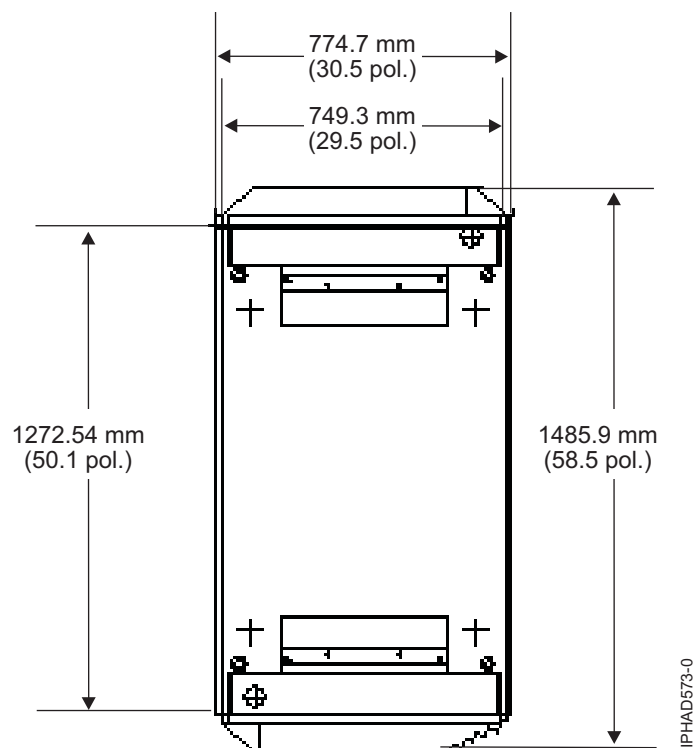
Vista de plano para sistema de estrutura única com portas slimline
